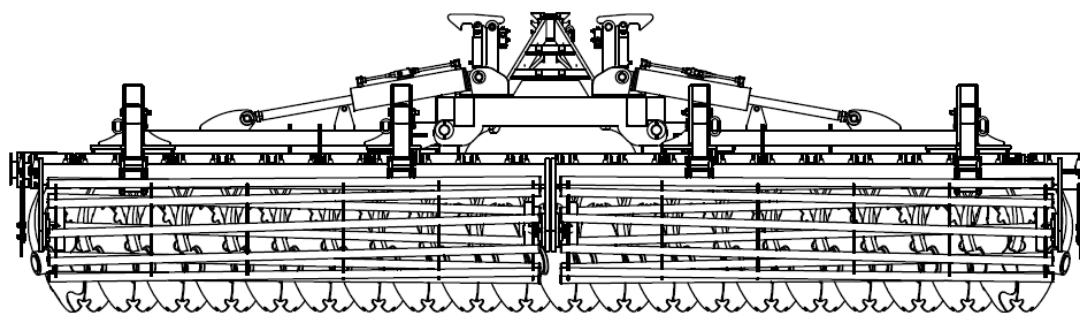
Vue de la machine à la fin de la séquence d'ouverture des ailes. Les bras de la machine sont entièrement ouverts.
